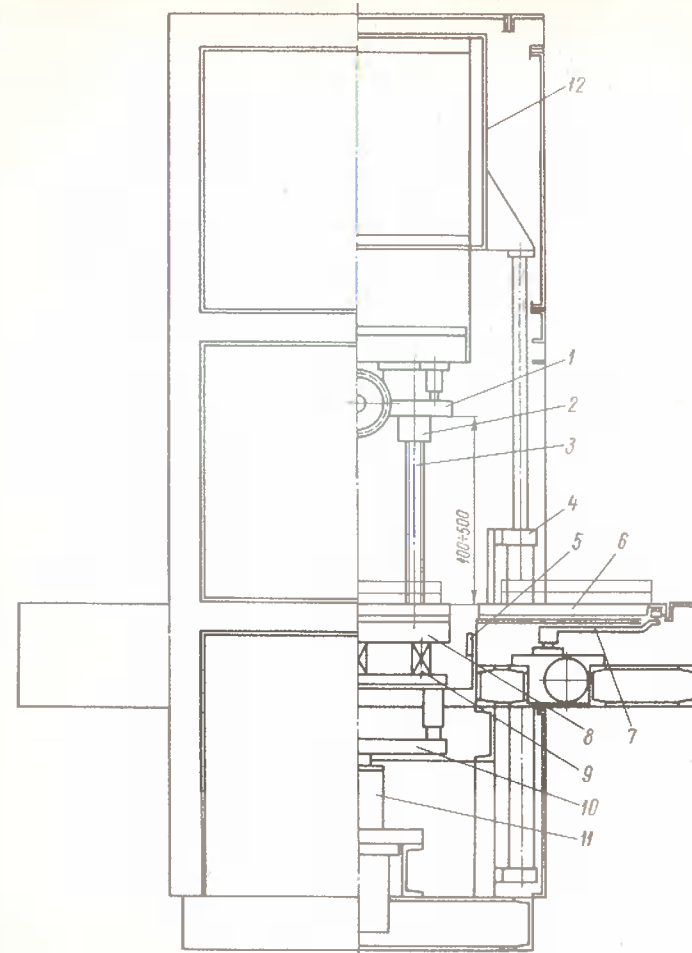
Конструкция ВЧ-пресса с двумя загрузочными столами для сварки объемных изделий
